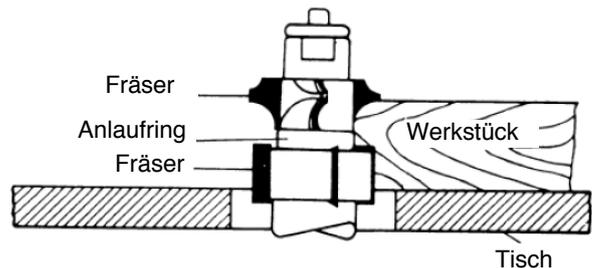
Fräsen mit Anlaufring zwischen zwei Fräsern
